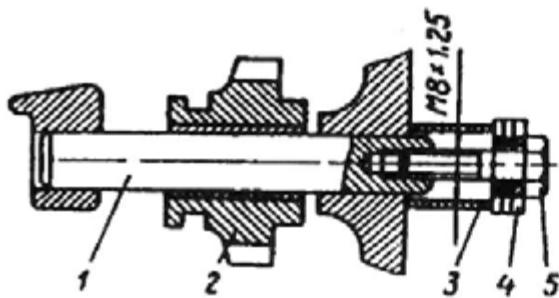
Выпрессовка оси промежуточной шестерни заднего хода:
